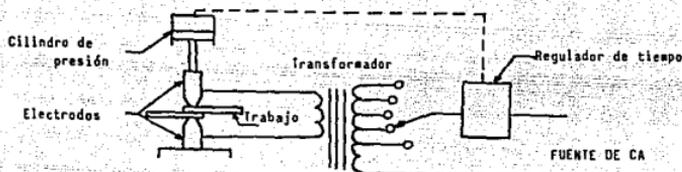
Circuito básico de soldadura por resistencia.
